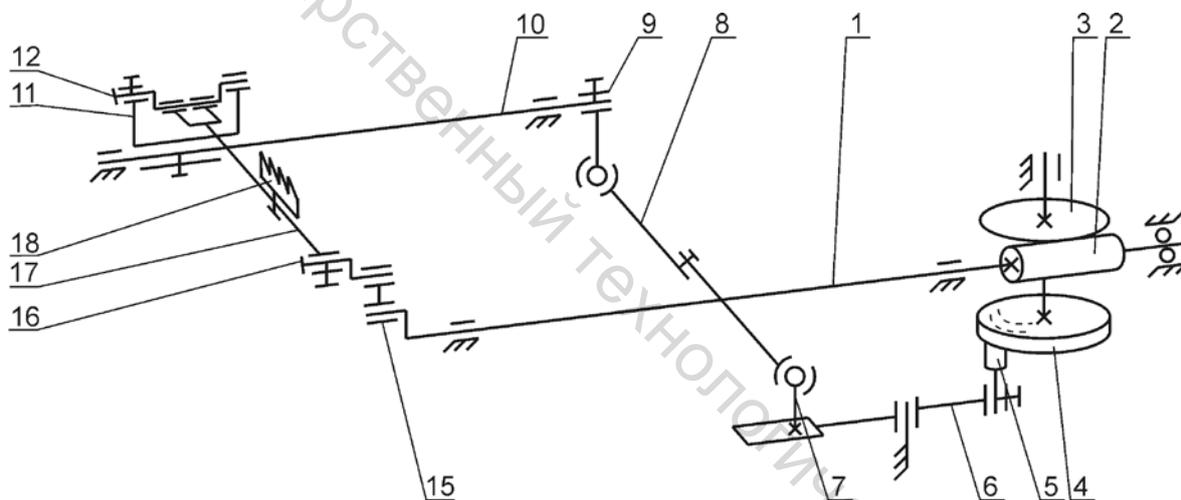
Кинематическая схема механизма рейки машины LZ-2285 Juki
